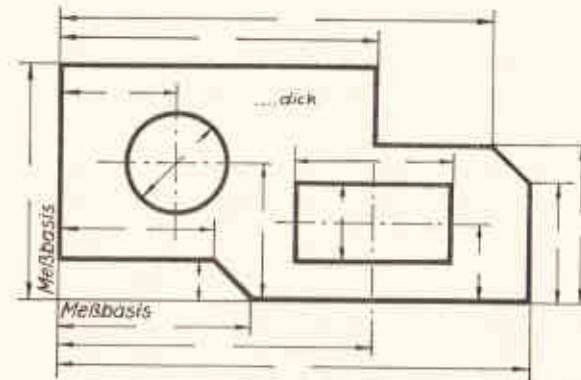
Bemaßen eines Werkstücks mit zwei Anlegekanten
